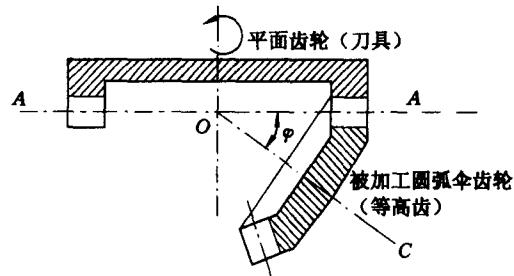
平面齿轮原理加工等高弧齿锥齿轮
